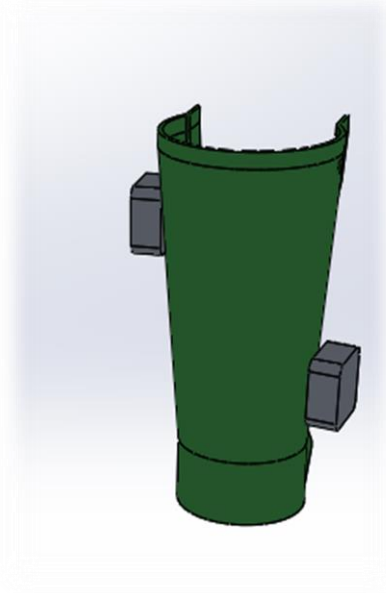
Dimensión de la pieza apoyo entre-pierna
